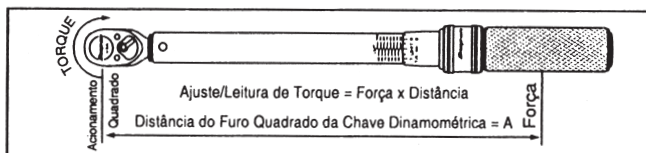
O torque do fixador é igual ao torque do furo quadrado da chave dinamométrica.
